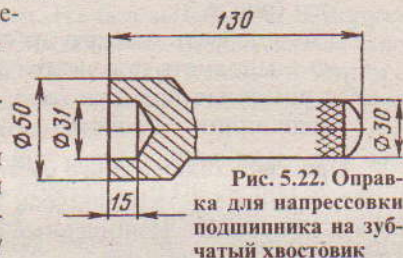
Оправка для напрессовки подшипника на зубчатый хвостовик
